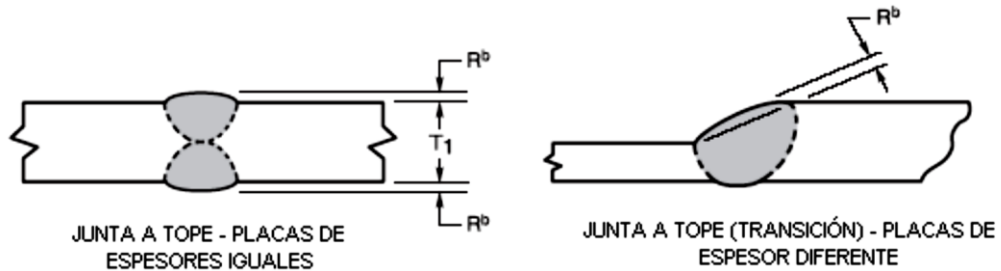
Perfiles aceptables de soldadura de ranura [4].
